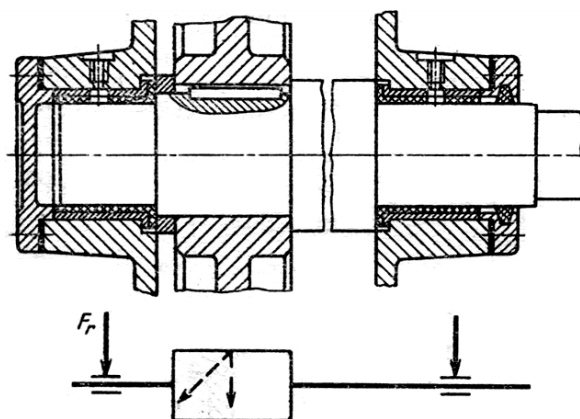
Расчетная схема цапфы тихоходного вала редуктора
